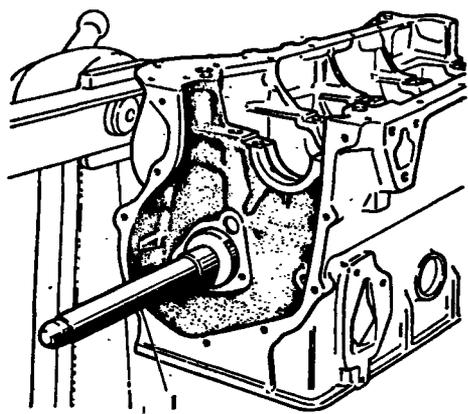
Снятие и установка втулок валика привода масляного насоса: 1 - оправка А.60333/1/2
